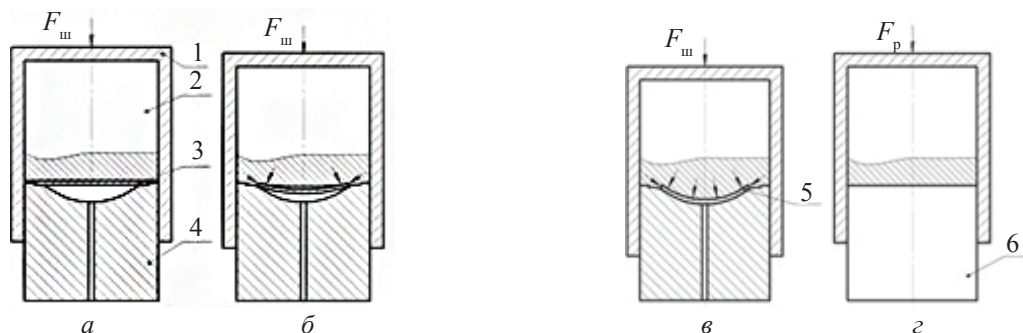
Стадии штамповки менисковой облицовки свинцом: а — исходное положение оснастки и заготовки; б — промежуточная стадия штамповки; в — завершающая стадия штамповки; г — разглаживание свинца; 1 — контейнер; 2 — свинец; 3 — заготовка; 4 — матрица; 5 — разглаживатель свинца
